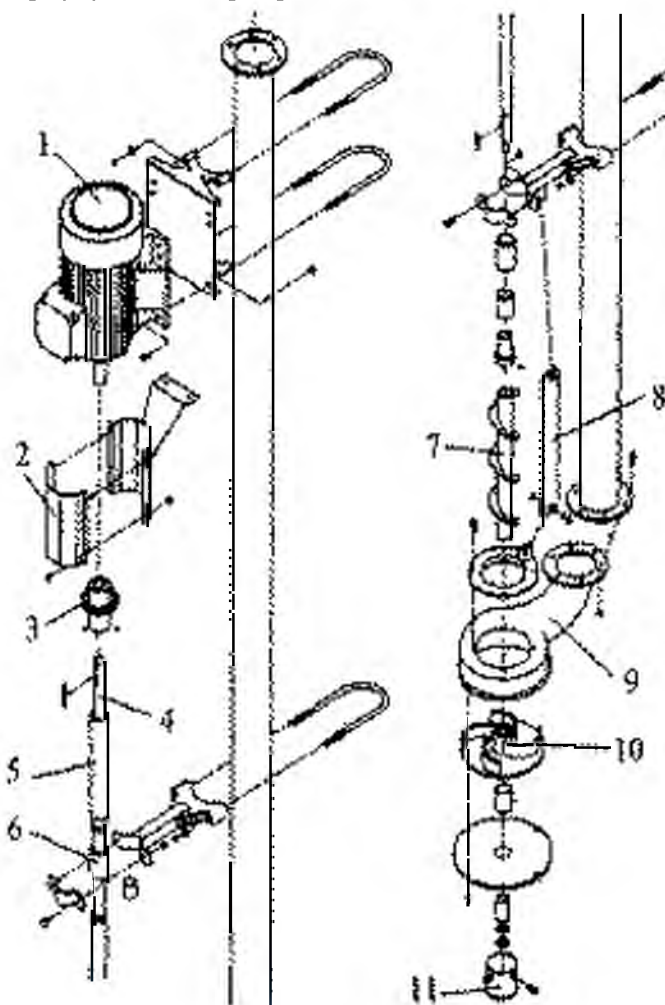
Центробежный насос фирмы Kitadan A/S:
